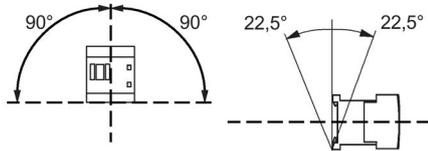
Posiciones de montaje de tamaños S6, S10, S12
